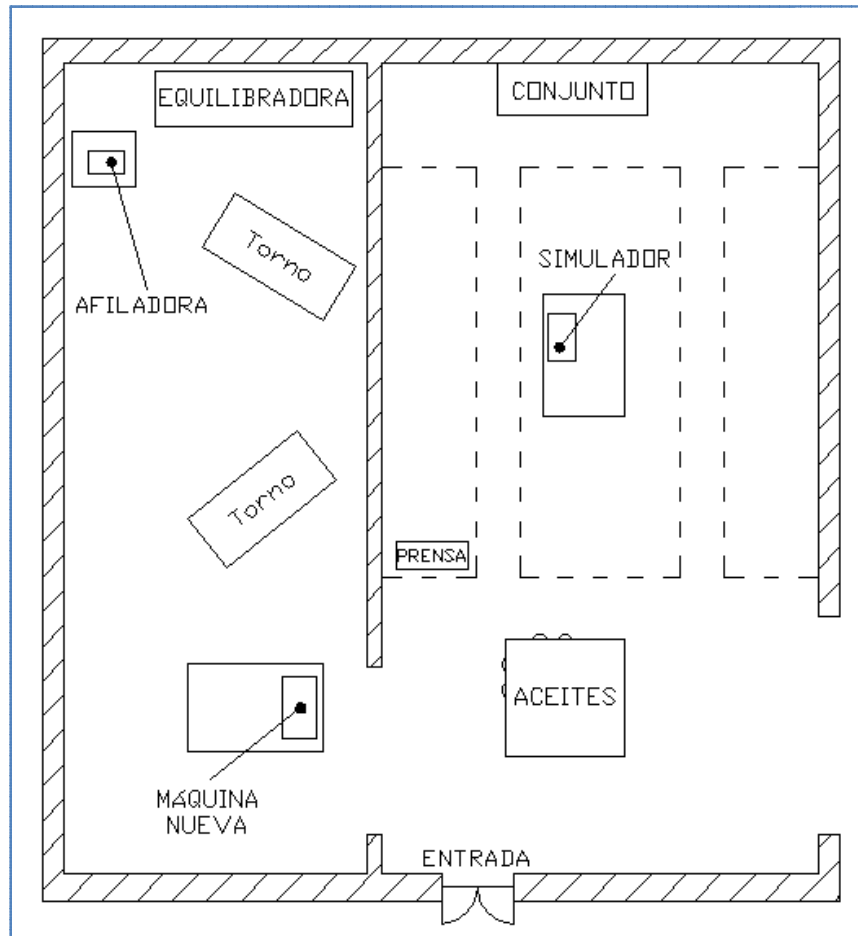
Croquis en planta de la 2ª distribución de zonas propuesta
